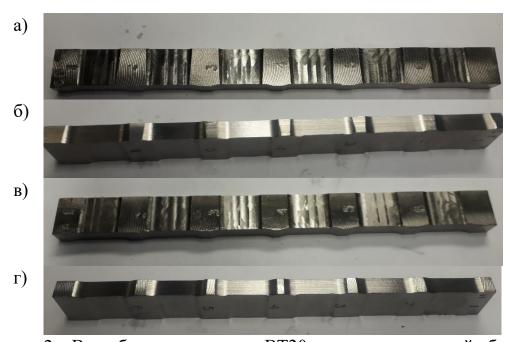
Вид образцов из сплава BT20 после механической обработки фрезерованием: а — торцевым; б — цилиндрическим фрезерованием изношенной фрезой; в — торцевым; г — цилиндрическим фрезерованием новой фрезой
